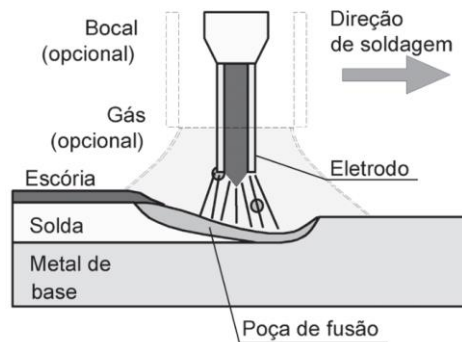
Processo de Soldagem Flux Core Arc Weld – FCAW, (Fonte: VILLANI *et al.*,2016).
